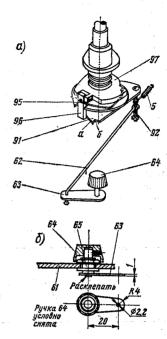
Кинематическая схема механизма Рис. 4. Кинематическая схема механизма повторного воспроизведения (a) и узел ручки управления (6); 5— пружина; 61— ланель; 62— тяга; 63— рычаг; 64— ручка управления; 65— втулка резьбовая (от резистора СП); 91— рычаг; 92— винт $M3 \times 10$; 95— пружина защелки; 96— защелка; 97— блок кулачков.
